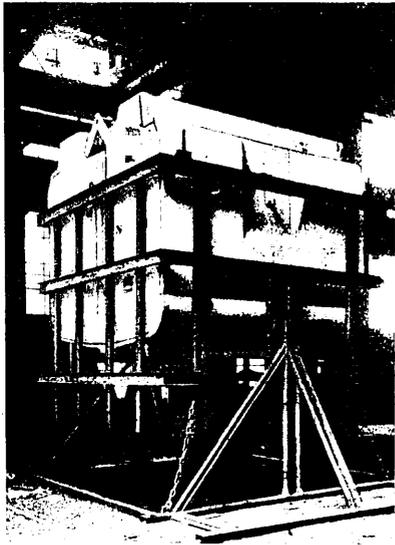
Kokskübel in der Schweißvorrichtung.
